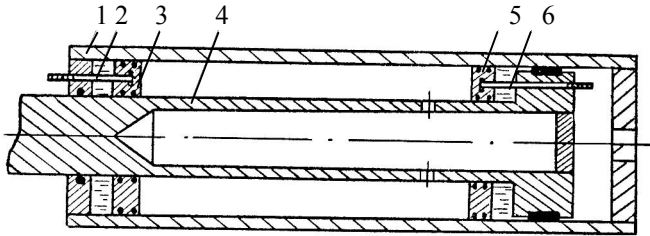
Схема пневматичного одноциліндрового накатника:
